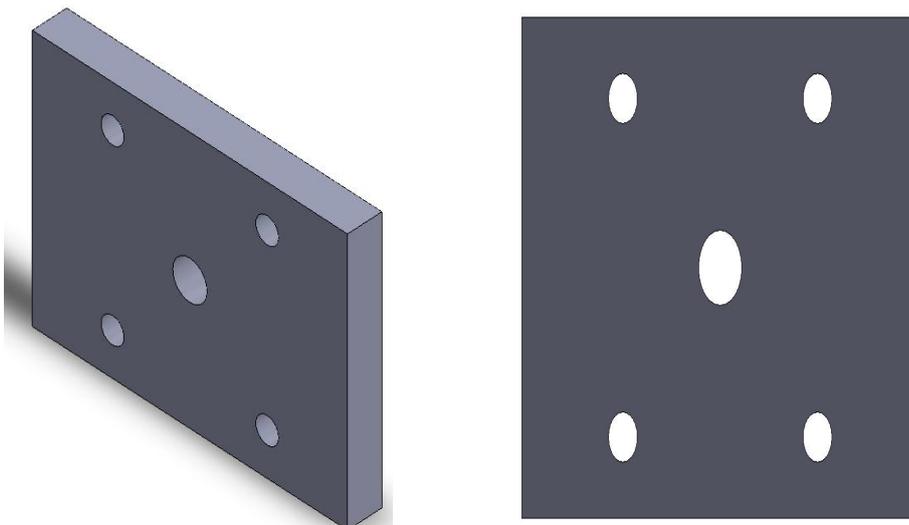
Pièce qui fixe le moteur sur le Châssis
